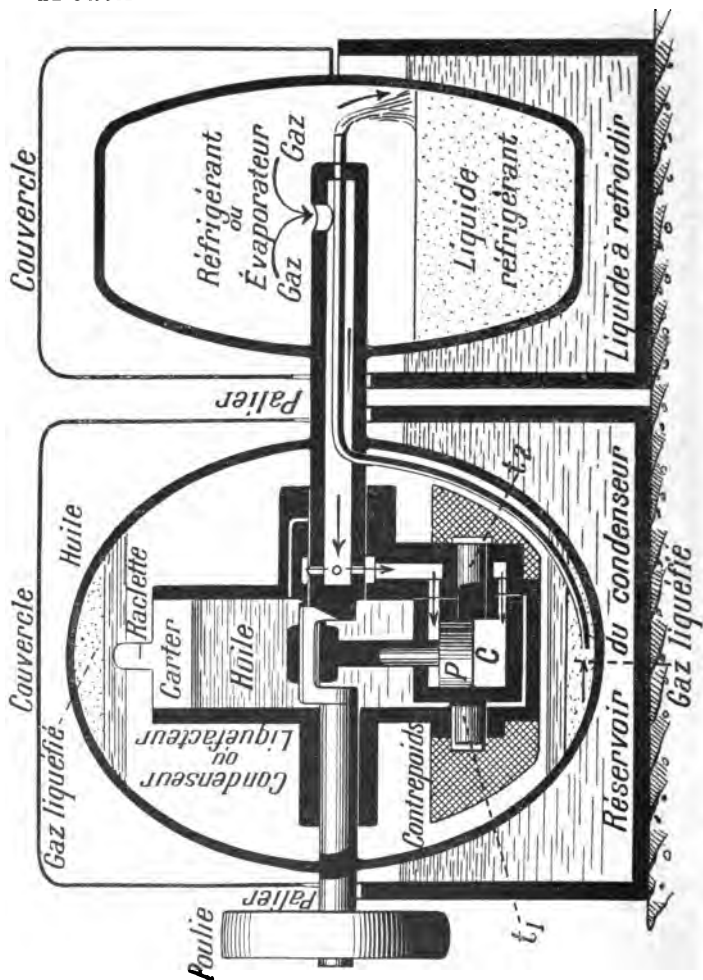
Coupe de la machine frigorifique Audiffren et Singrün.
